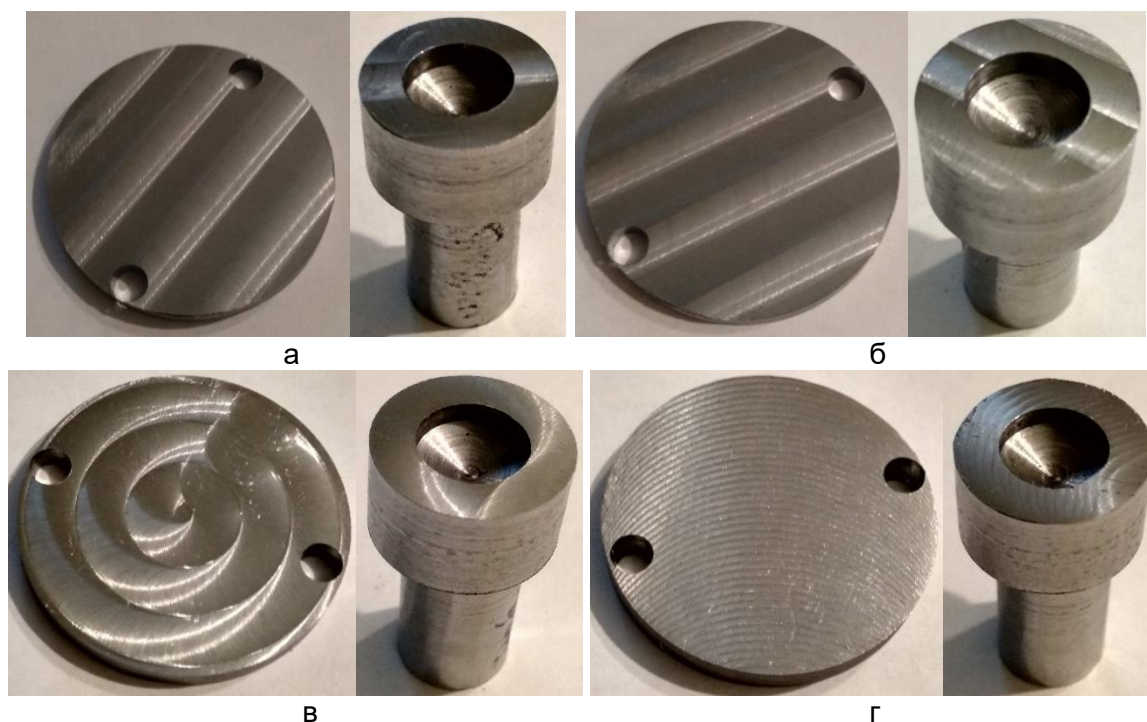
Образцы (нижний – «диск», верхний – «подпятник»), полученные различными технологиями фрезерования: попутным фрезерованием параллельными проходами (а); попутно-встречным фрезерованием по зигзагообразной траектории (б); непрерывным попутным фрезерованием от периферии к центру (в); трохоидальным фрезерованием (г)
